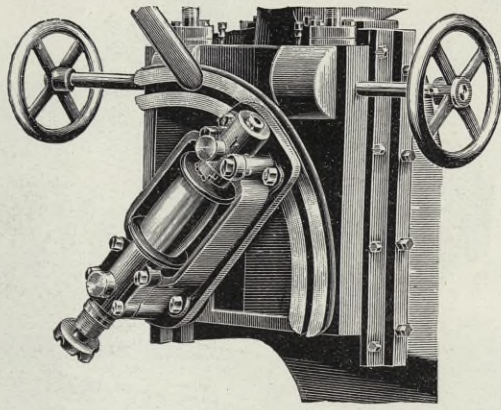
Oberer Teil der Fräsmaschine mit Schrägstellung der Frässpindel unter 45° .
